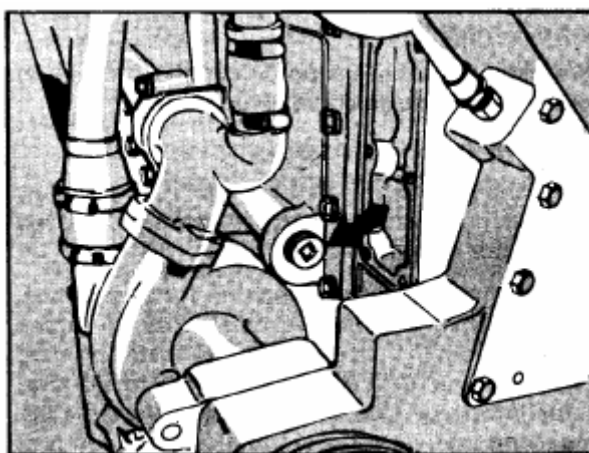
(OM1004L). Точка заливки системы смазки - двигатель KT / KTA19 C.I.D
